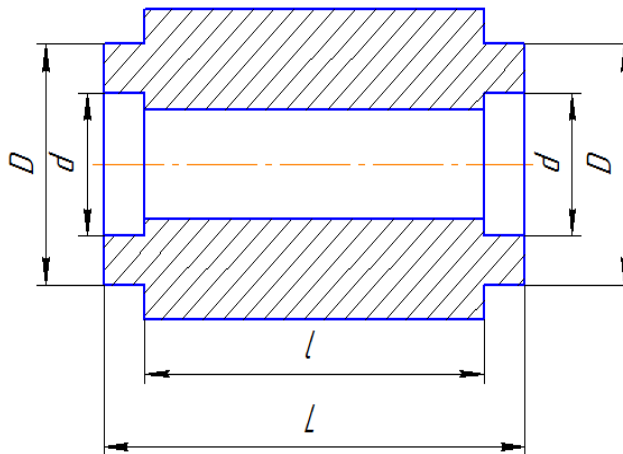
Эскиз заготовки с кольцевыми выступами на торцах
